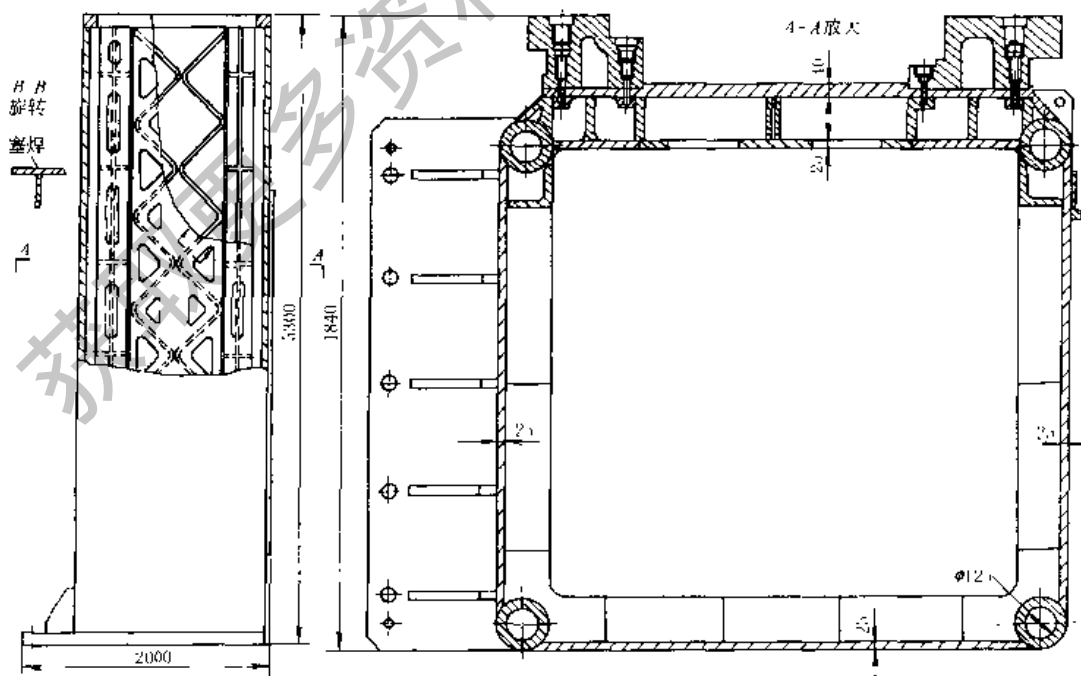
大型落地镗铣床的焊接立柱
